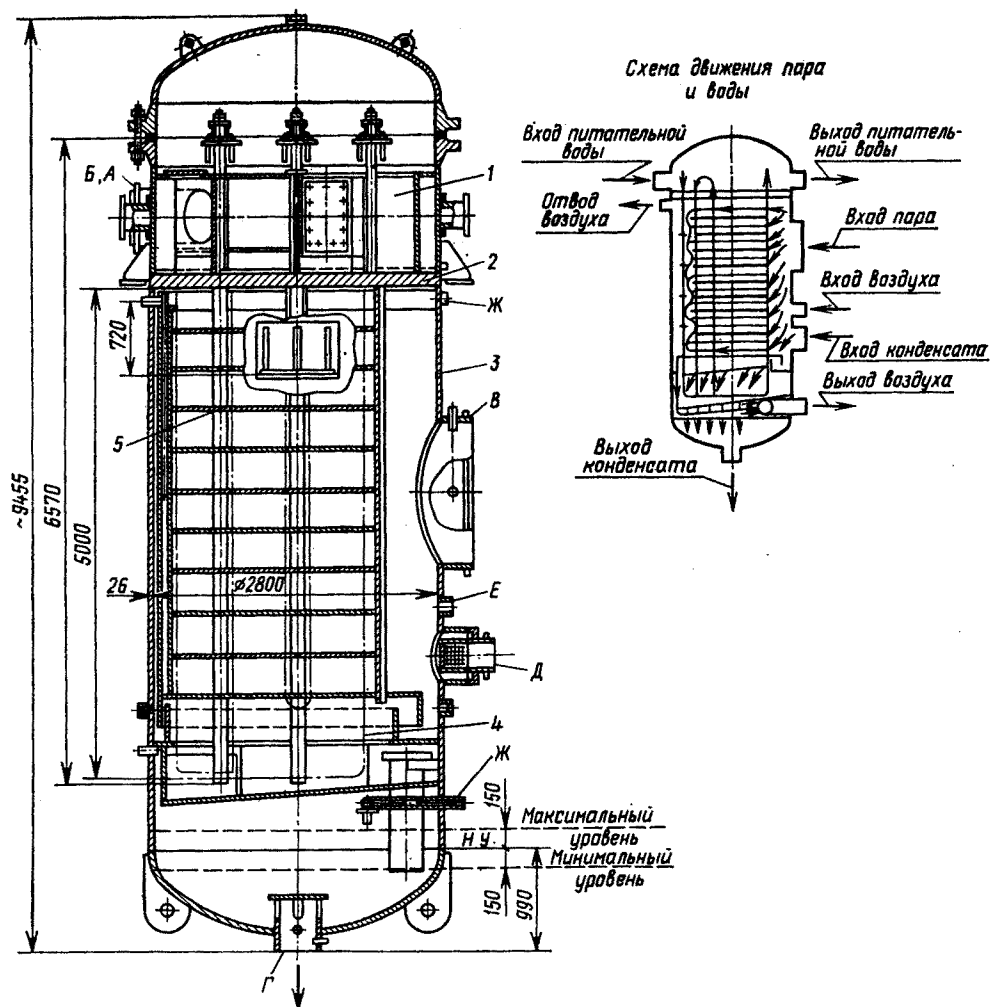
Подогреватель ПН-2300-25-7-IV:
